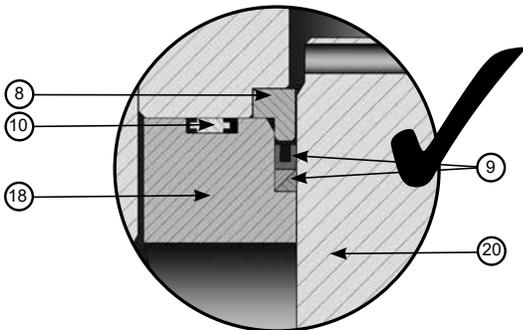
В. Правильная установка уплотнительного кольца, при которой прямой угол нижнего опорного кольца обращен к экструзионному зазору
